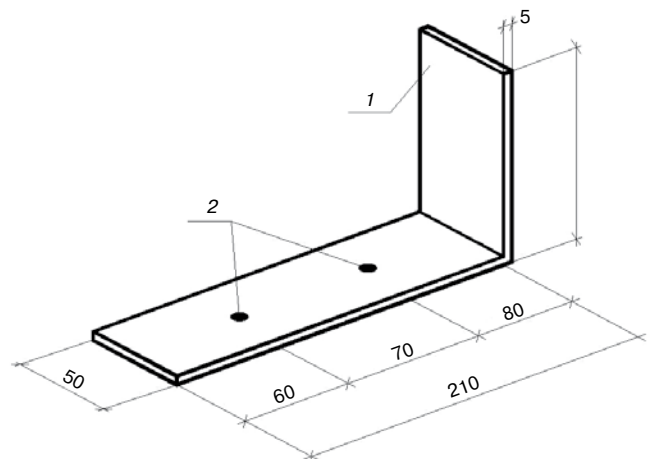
Соединительный элемент: 1 – оцинкованная пластина; 2 – отверстия под нагели $\varnothing 5$ мм
